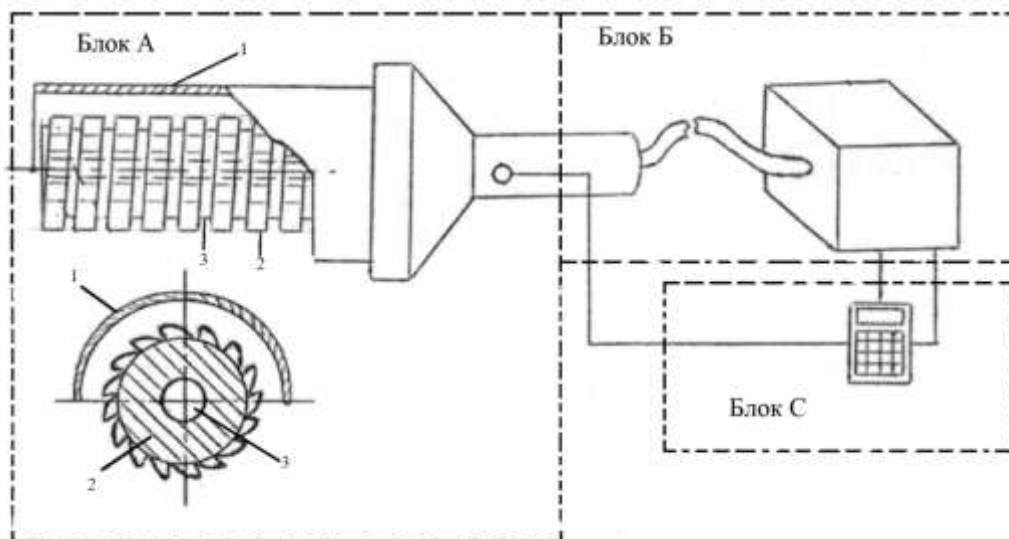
Общий вид устройства для чистки рыбы от чешуи
